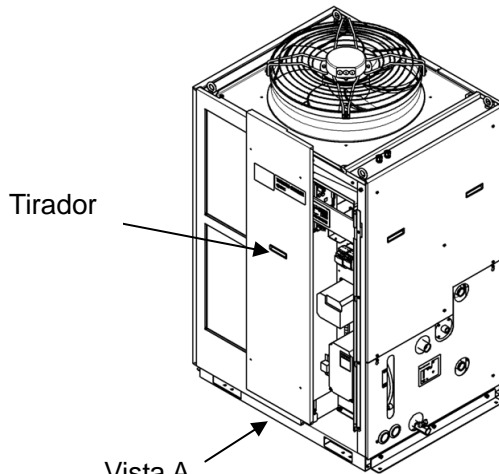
Retirada del panel frontal de la unidad eléctrica
